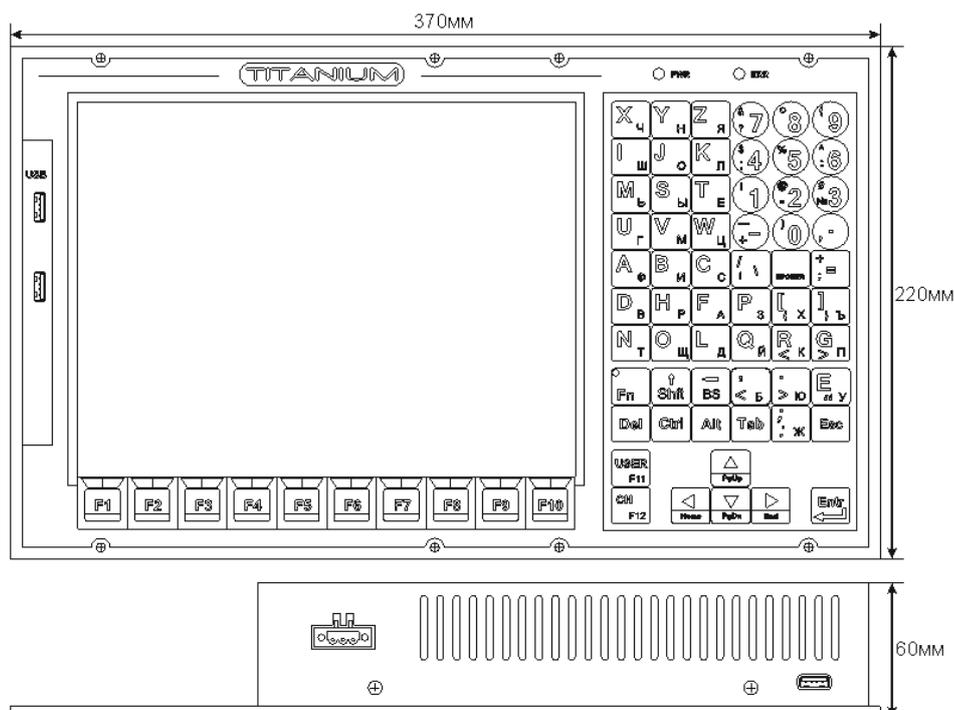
габаритный размер блока ЧПУ TITANIUM
